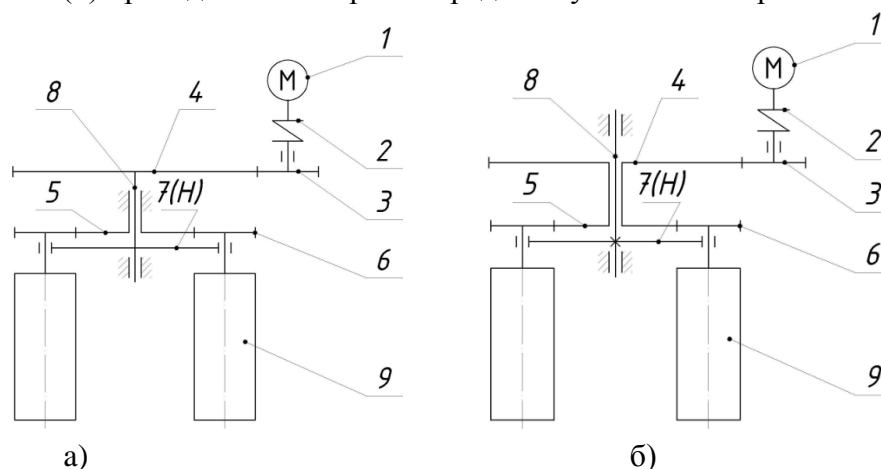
Кинематическая схема планетарного механизма редукторного (а) и мультипликаторного (б) типа, где: 1 – электродвигатель, 2 – муфта, 3 – шестерня, 4 –
